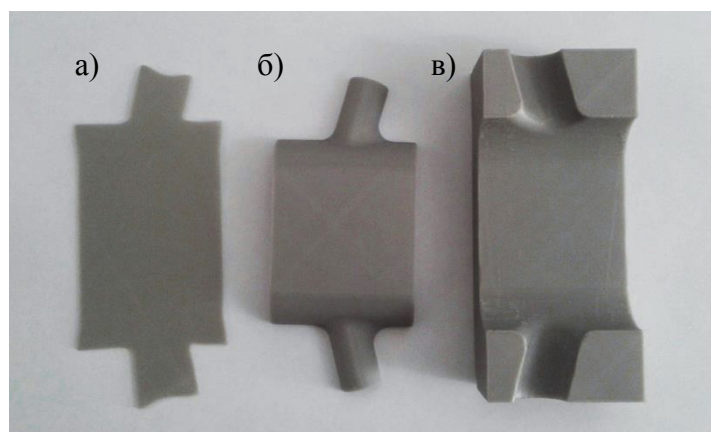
Оснастка, изготовленная методом трехмерной печати:
